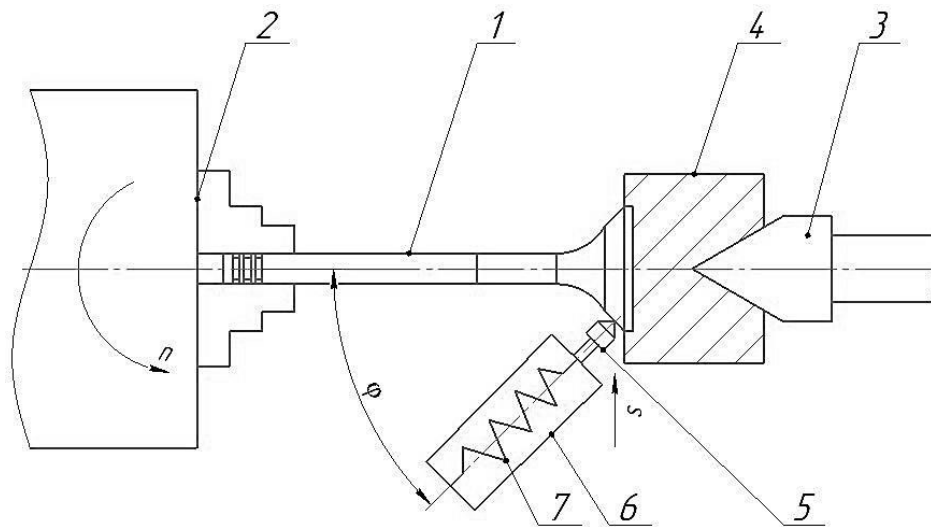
Схема алмазного вигладжування: 1 – оброблюваний клапан; 2 – трикулачковий патрон; 3 – центр обертання; 4 – оправка центруюча; 5 – алмазний вигладжувач; 6 – корпус; 7 – пружина з регулюванням підтискання.
